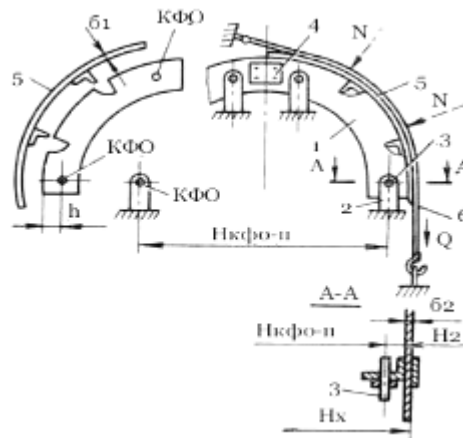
Базирование по КФО: 1 – шпангоут; 2 – вилка; 3- фиксатор; 4 – накладка; 5 – панель; 6 – лента.
